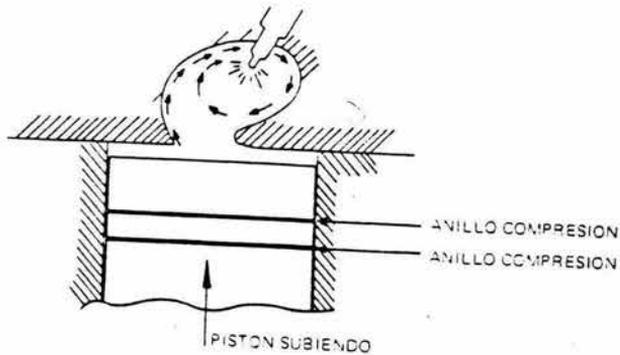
Inyección Indirecta. La inyección se hace en la Cámara de Combustión Maquinada en la Cabeza del Motor fuera del Cilindro.
